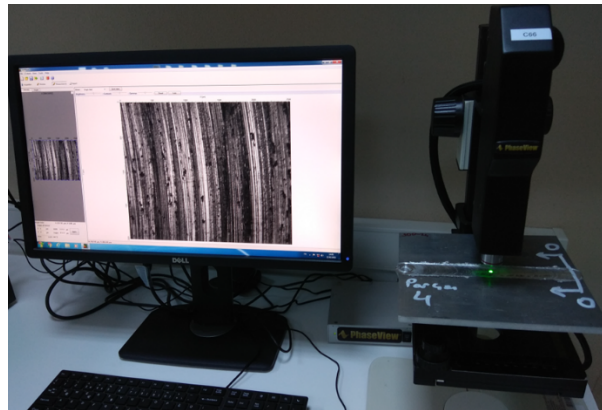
Sürtünme karıştırma kaynağı uygulaması (Friction stir welding application)
